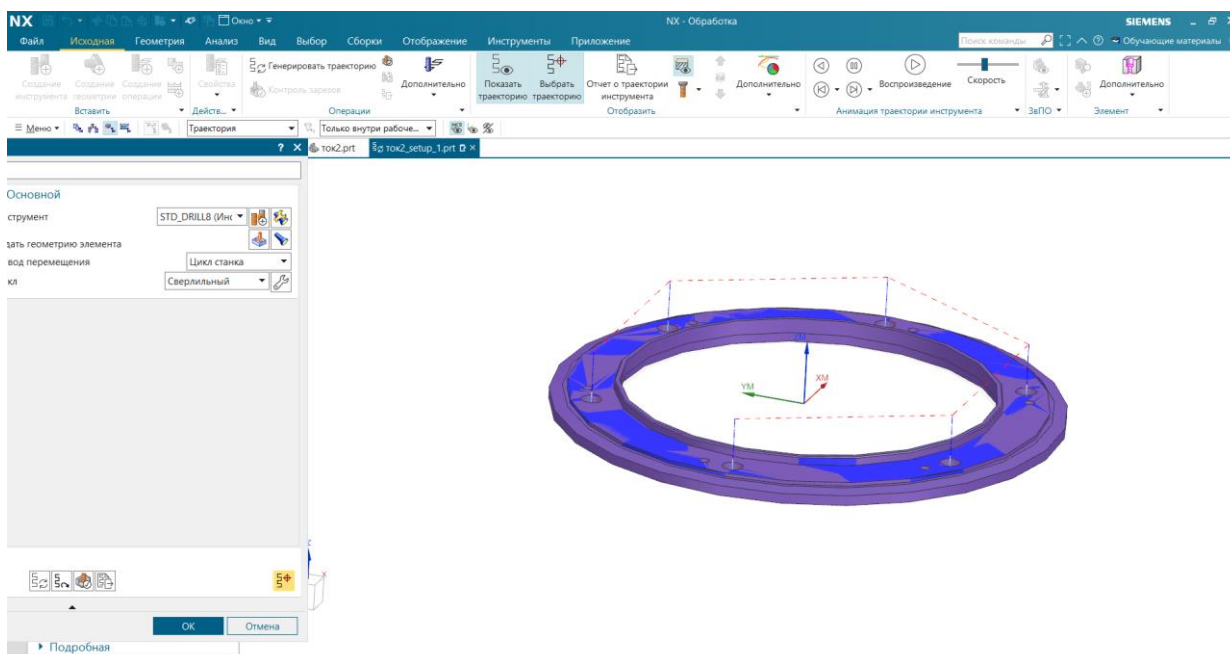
Визначення деталі, заготовки в системі NX CAM
